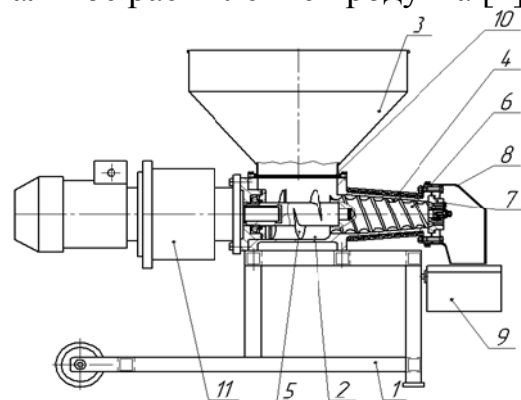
Шнековый экструдер-гранулятор: 1 – рама; 2 – приемная камера; 3 – приемный бункер; 4 – рабочая камера; 5 – подающий шнек; 6 – прессующий шнек; 7 – узел прессования; 8 – короб; 9 – сборник; 10 – заслонка; 11 – мотор-редуктор
